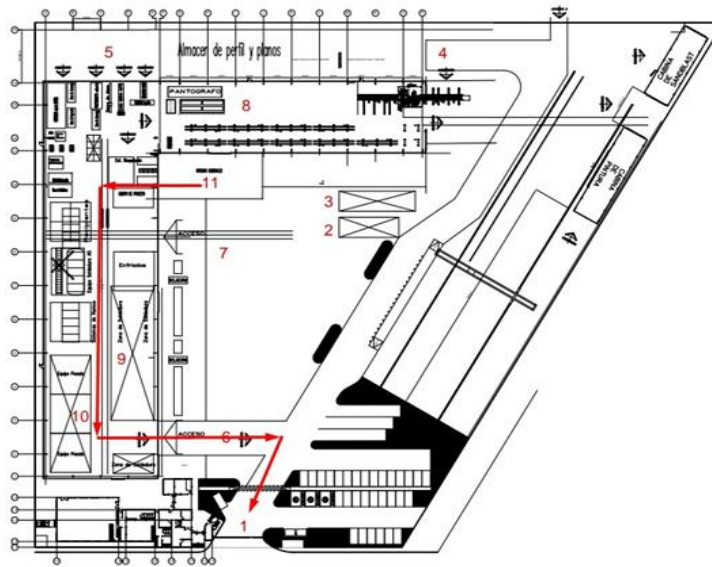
Layout prueba 1 de la Planta Durosa Santa Rosa SA, de CV.
